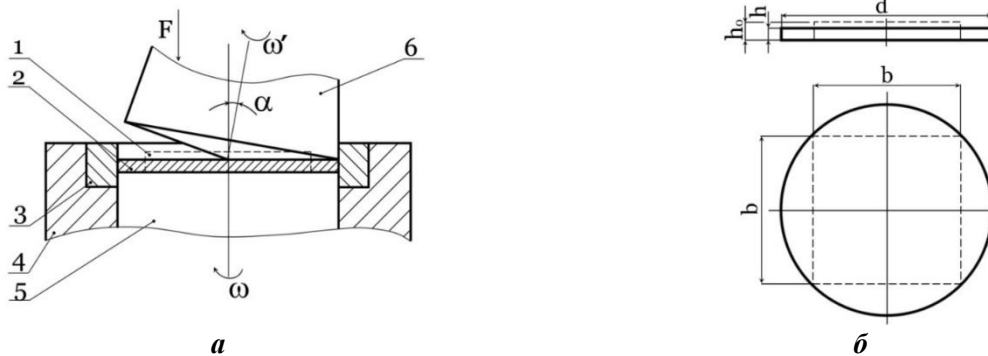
Схема переформування заготовок методом ШО (а), вид вихідної квадратної і переформованої круглої заготовки (б): 1 – заготовка, 2 – виріб, 3 – матриця, 4 – шпиндель, 5 – штовхач, 6 – валок.
